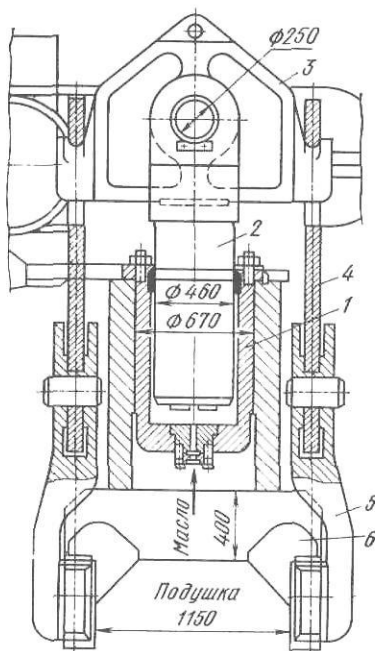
Гидравлическое уравнивание верхнего опорного валка стана 2500 при помощи одного верхнего гидроцилиндра
